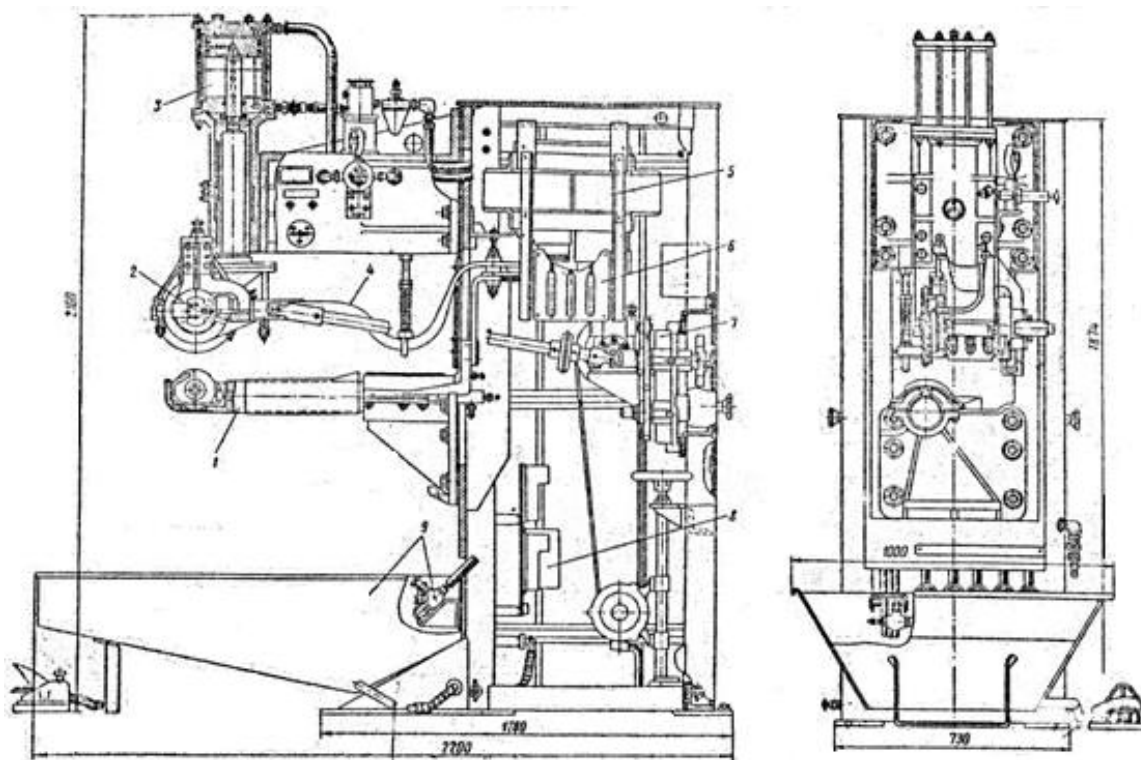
Общий вид машины шовной контактной сварки
